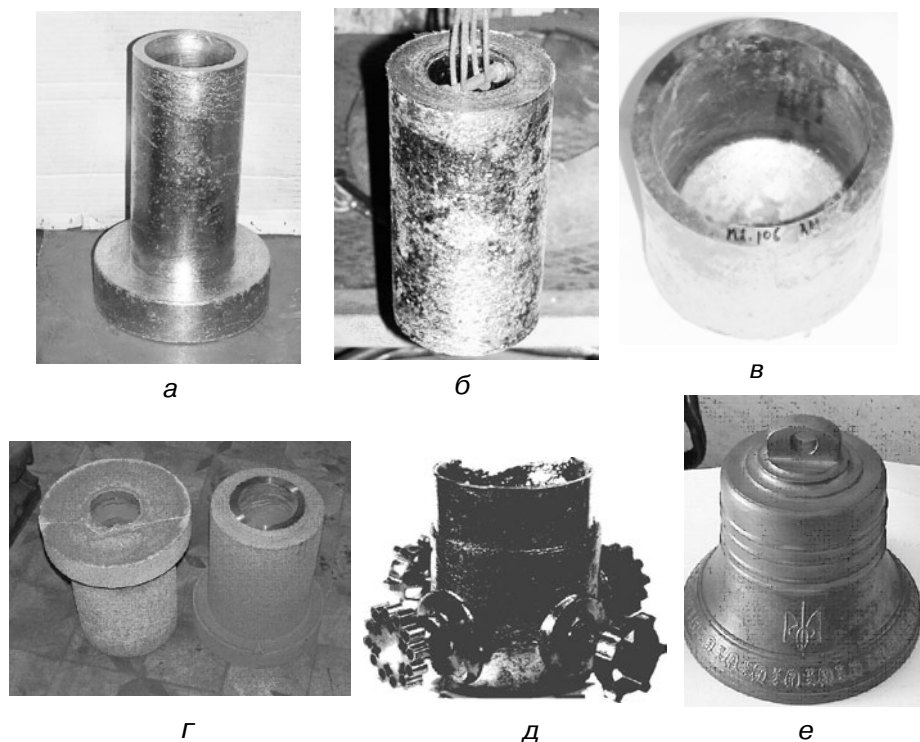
Центробежнолитые изделия электронно-лучевой выплавки: а – медная форма для литья трубной заготовки; б – трубная заготовка из стали; в – корпус контейнера для захоронения радиоактивных отходов, сплав ВТ1-0; г – трубные заготовки из сплава ВТ1-0; д – детали несущих конструкций ТВЭЛов; е – колокол из циркония
